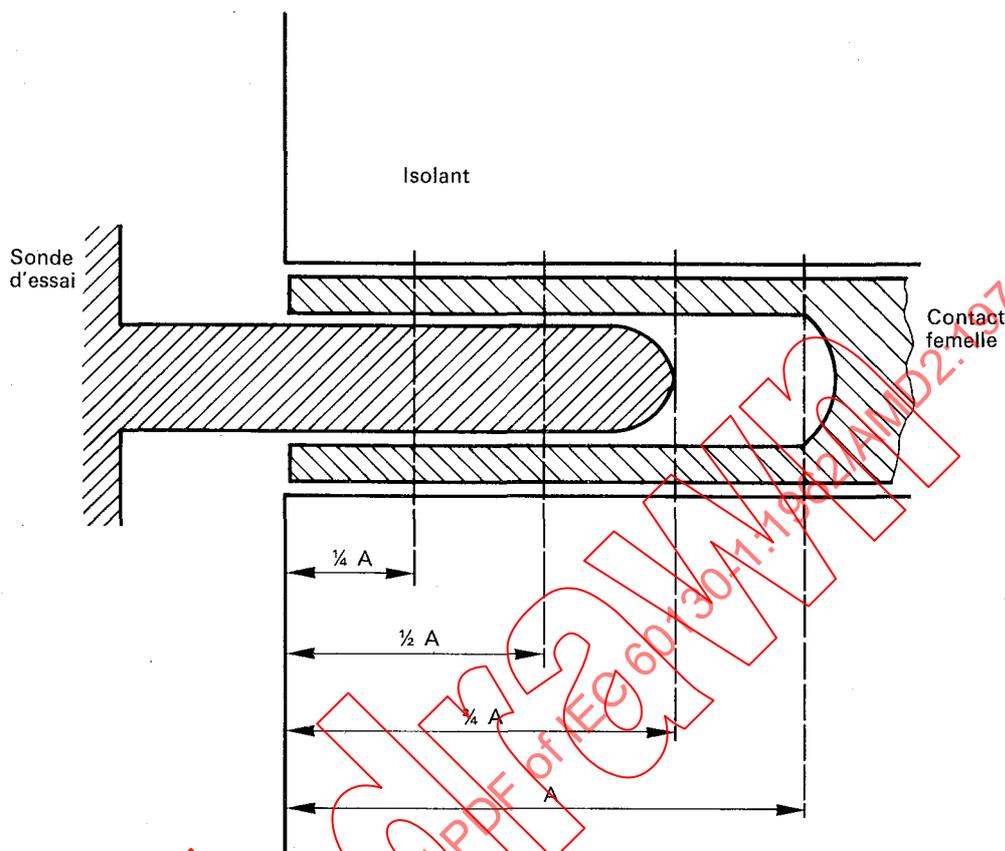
Coupe transversale de l'insertion de la sonde d'essai.
